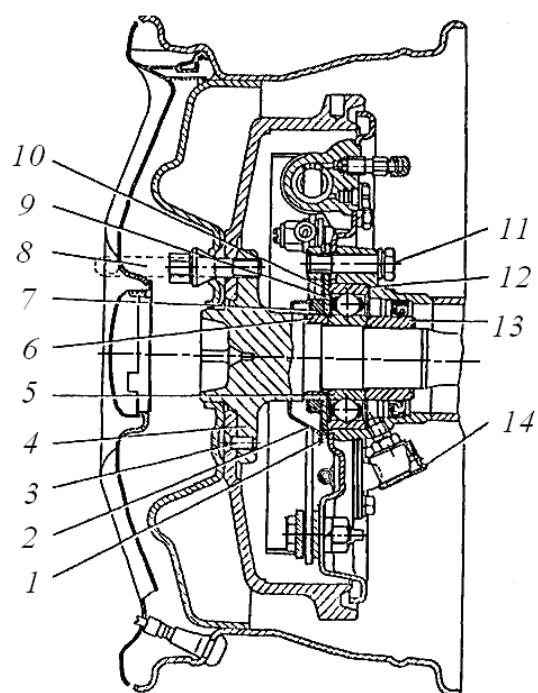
Задний мост (наружная часть): 1 – уплотнительная прокладка; 2 – маслоотражатель; 3 – винт крепления тормозного барабана; 4 – полуось; 5 – подшипник полуоси; 6 – втулка; 7 – войлочный уплотнитель; 8 – установочная шпилька (болт крепления колеса); 9 – 10 пластина; 11 – болт; 12 – пружинное кольцо; 13 – задняя втулка; 14 – колпачковая масленка
